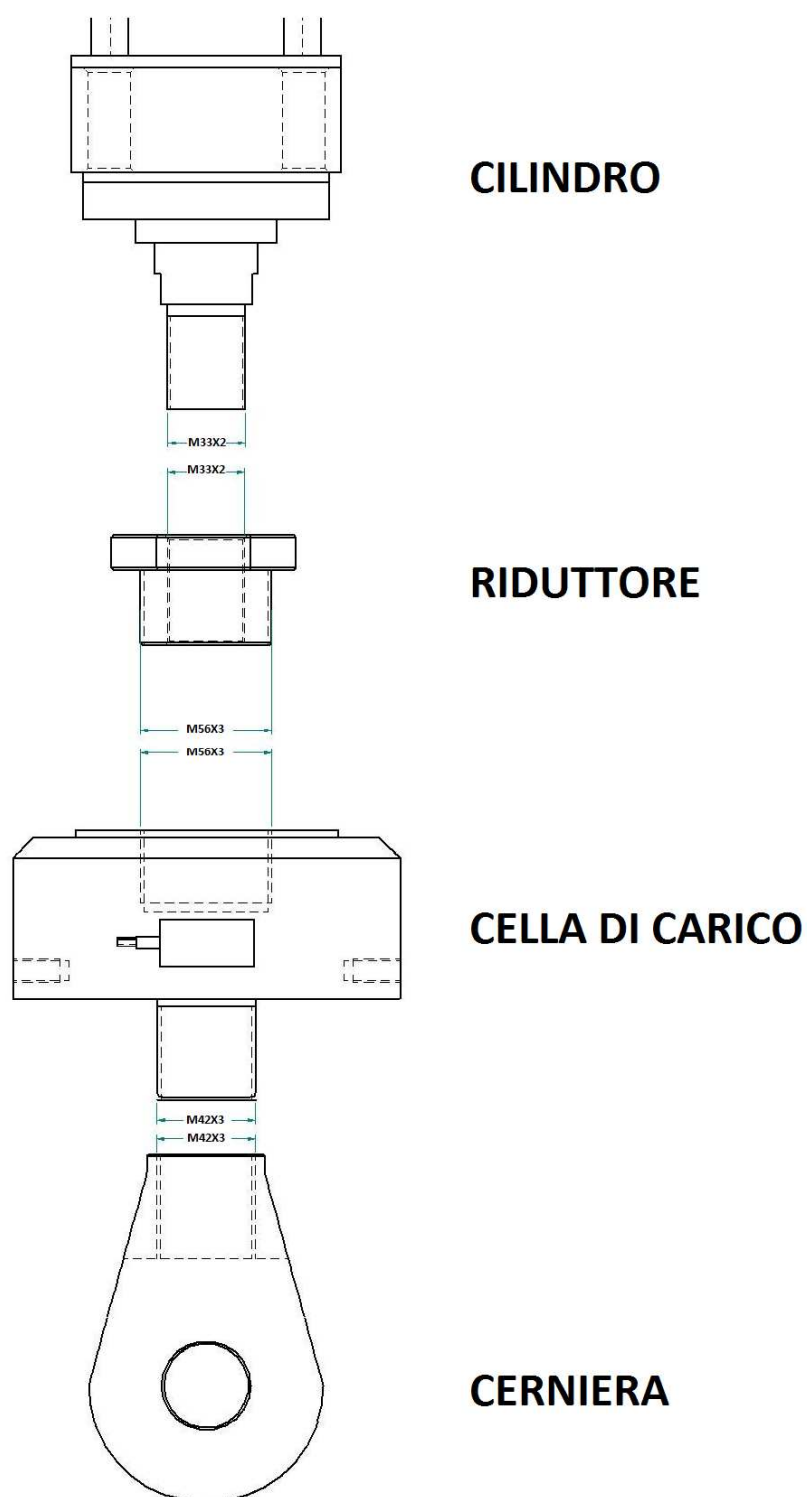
Schema di montaggio cilindro-riduttore-cella di carico-cerniera
